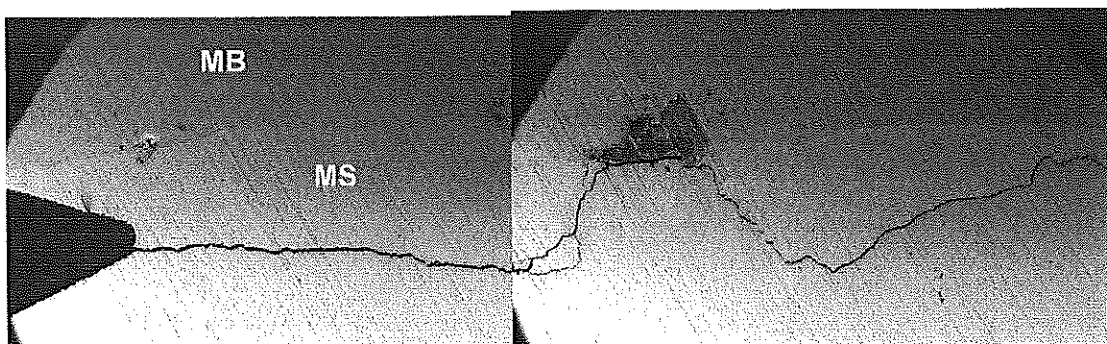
Imagen lateral del espécimen 3 donde se observa el inicio del crecimiento de grieta en fatiga (parte izquierda). También se observa que el inicio y crecimiento de esta fisura fue en el metal de soldadura.
